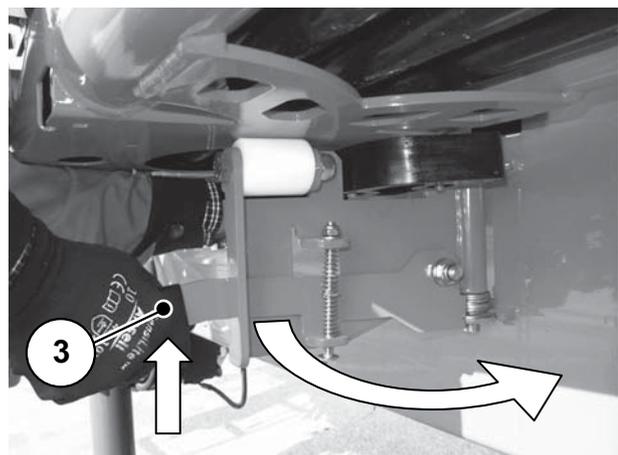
Levier en dessous de la conduite d'air de devant
